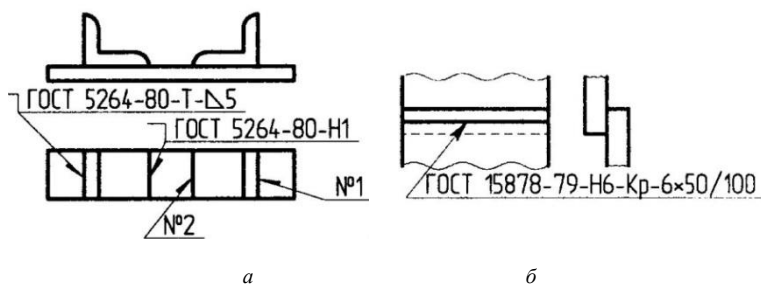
Обозначения сварных швов: *а* – сварка электродуговая сплошным швом; *б* – сварка контактная прерывистым швом
